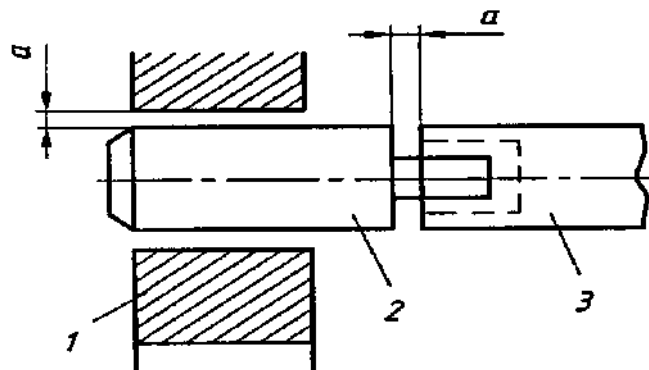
Установка вставки стержня сварной короткозамкнутой обмотки:
